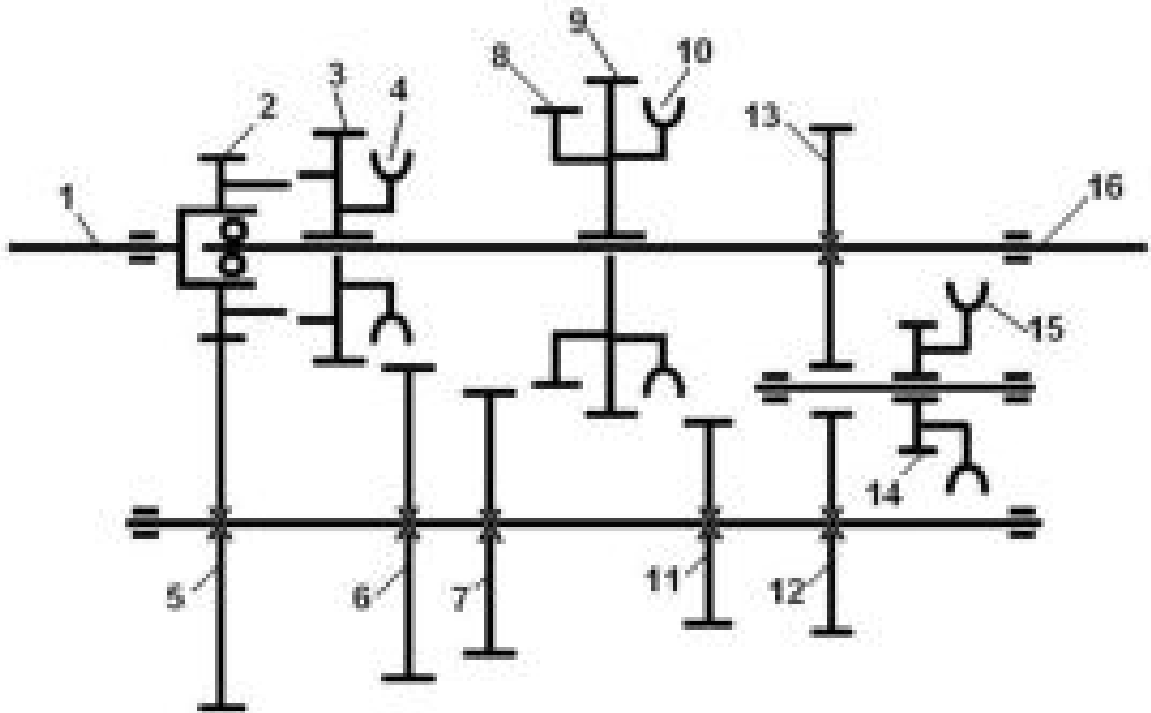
Кинематическая схема четырехступенчатой трехвальной коробки передач.
